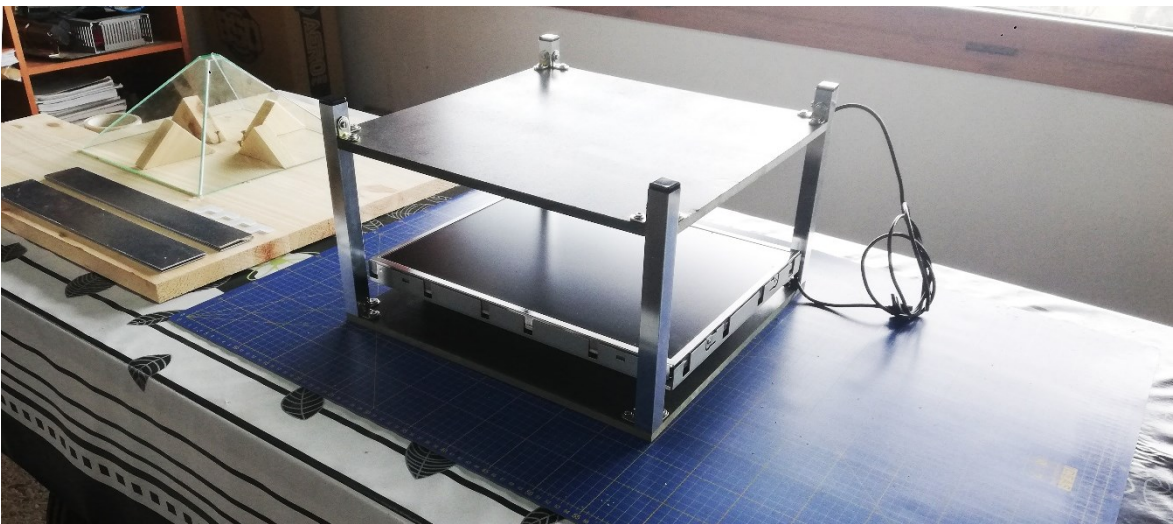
Anclaje de la base inferior del dispositivo.
